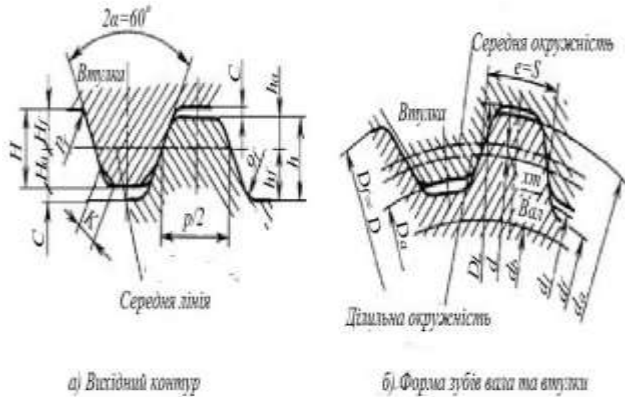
Центрування по бокових поверхнях зубів (плоска форма дна западини)
